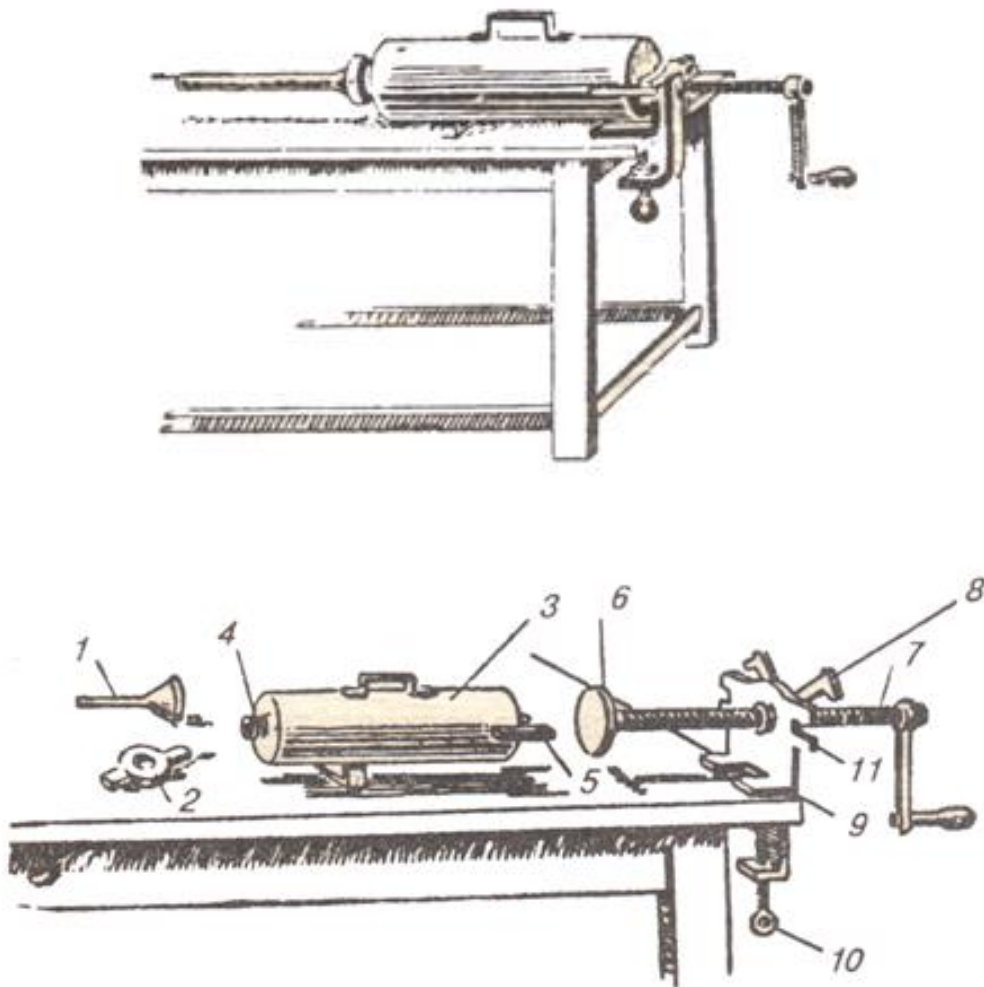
г. Устройство ручного станка для набивки оболочек.
